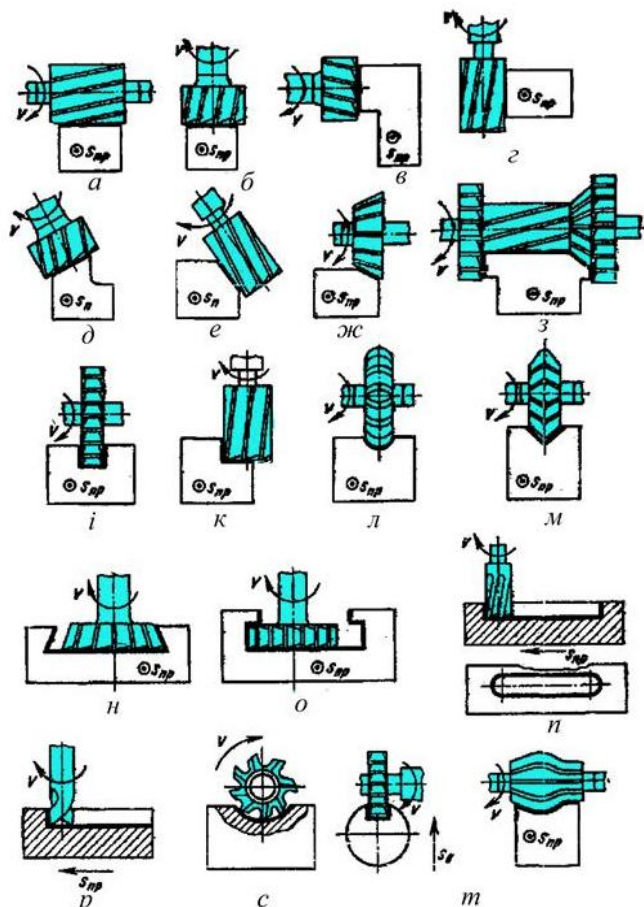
Схеми обробки поверхнь заготовок на горизонтально- та вертикально-фрезерних верстатах
